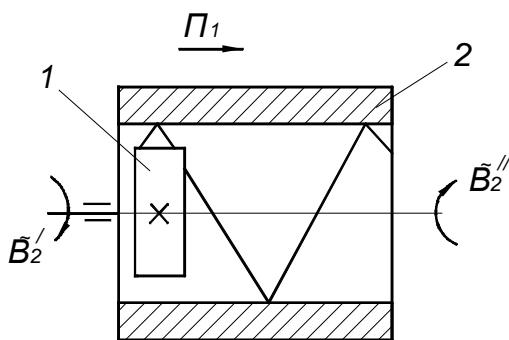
Схема нарезания винтовой канавки переменного шага
